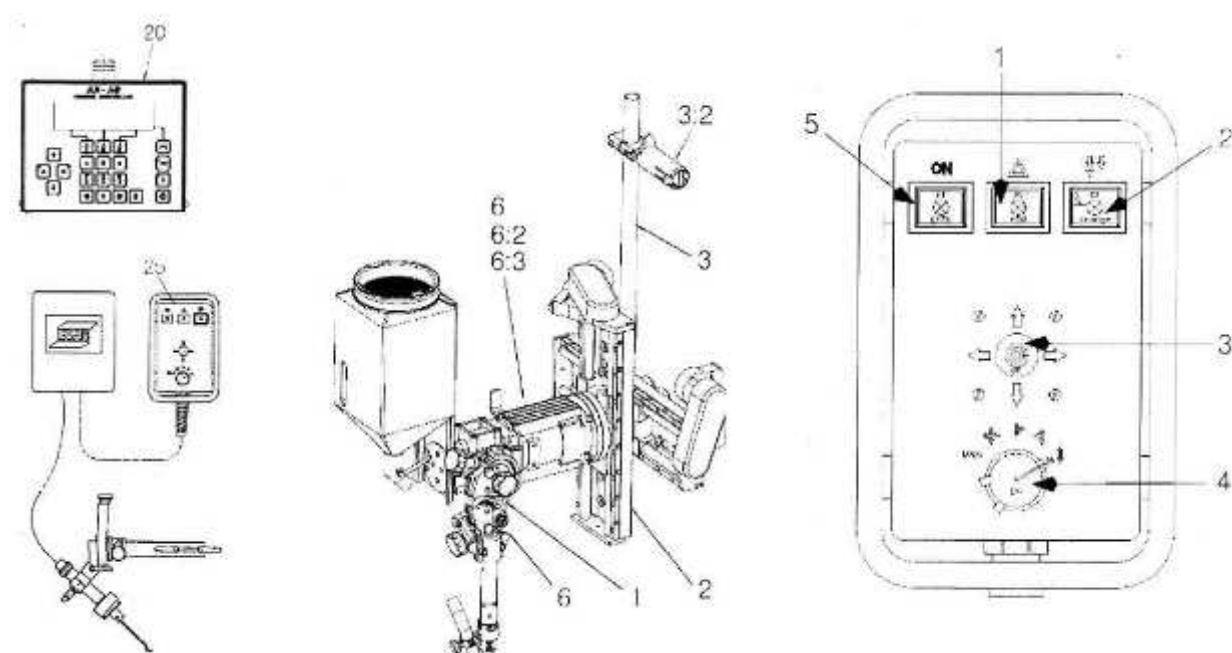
Сварочная головка A2 SAW для сварки под слоем флюса:
